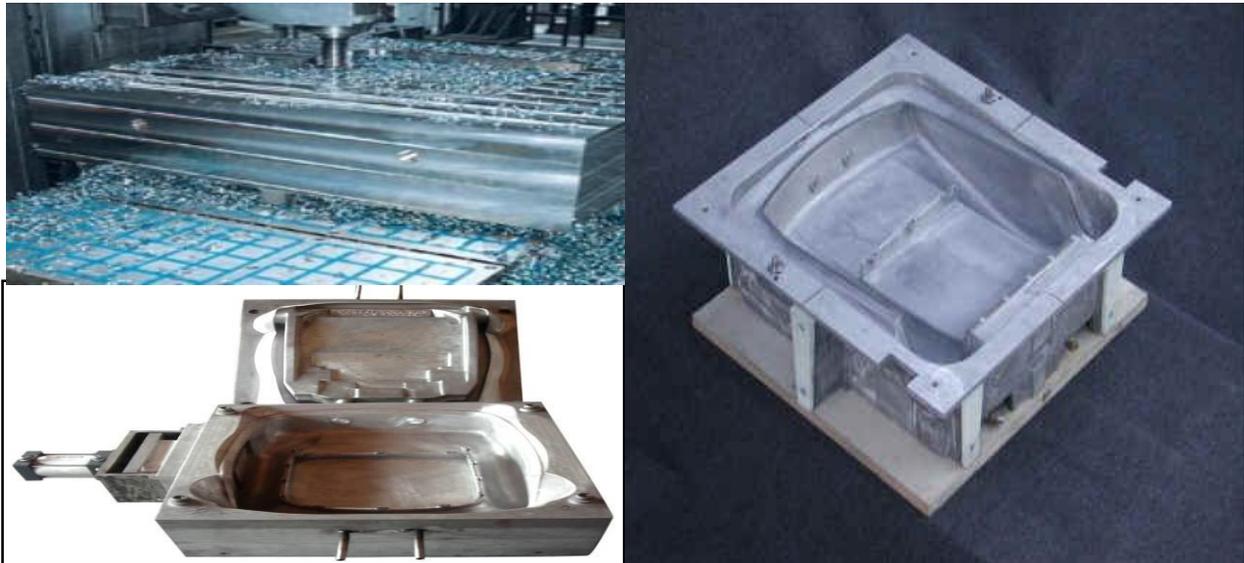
Superior: Mecanizado del molde. Inferior y Derecha: Muestra de un molde ya mecanizado “en caja”.
